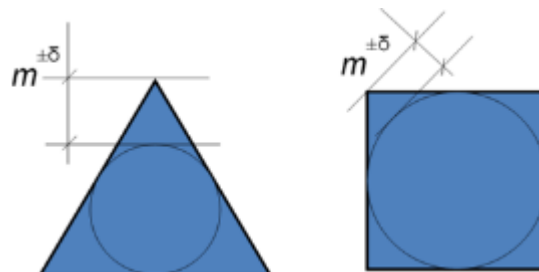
Допуск на відстань m від вершини до кола
